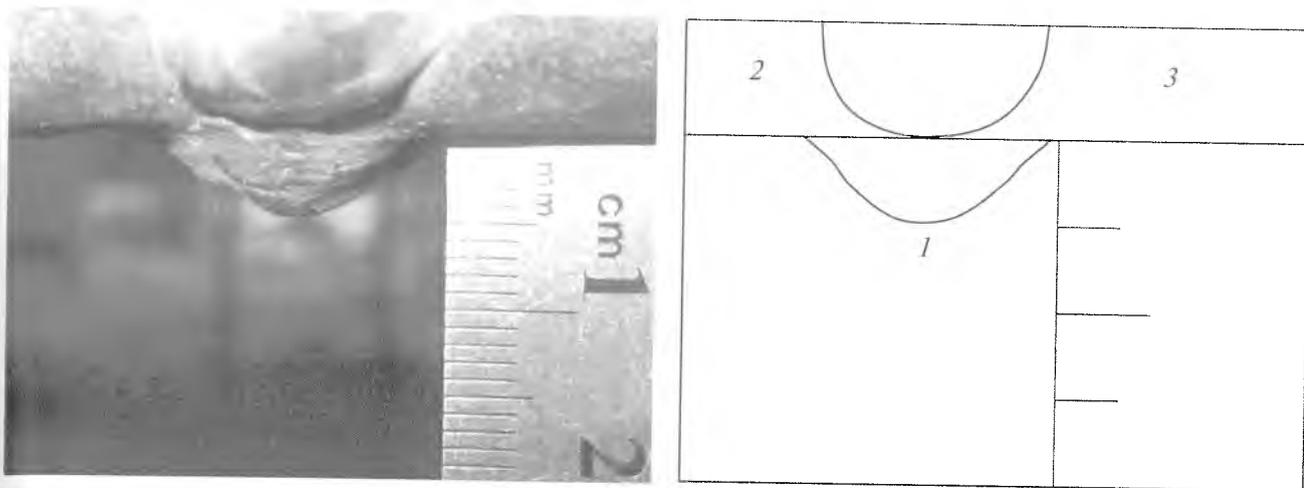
Выпуклость шва *1* – часть стыкового сварного шва, выступающая над уровнем поверхностей сваренных деталей *2* и *3*, в сварном соединении профиля квадратного сечения строительной конструкции. Вид вдоль оси шва
